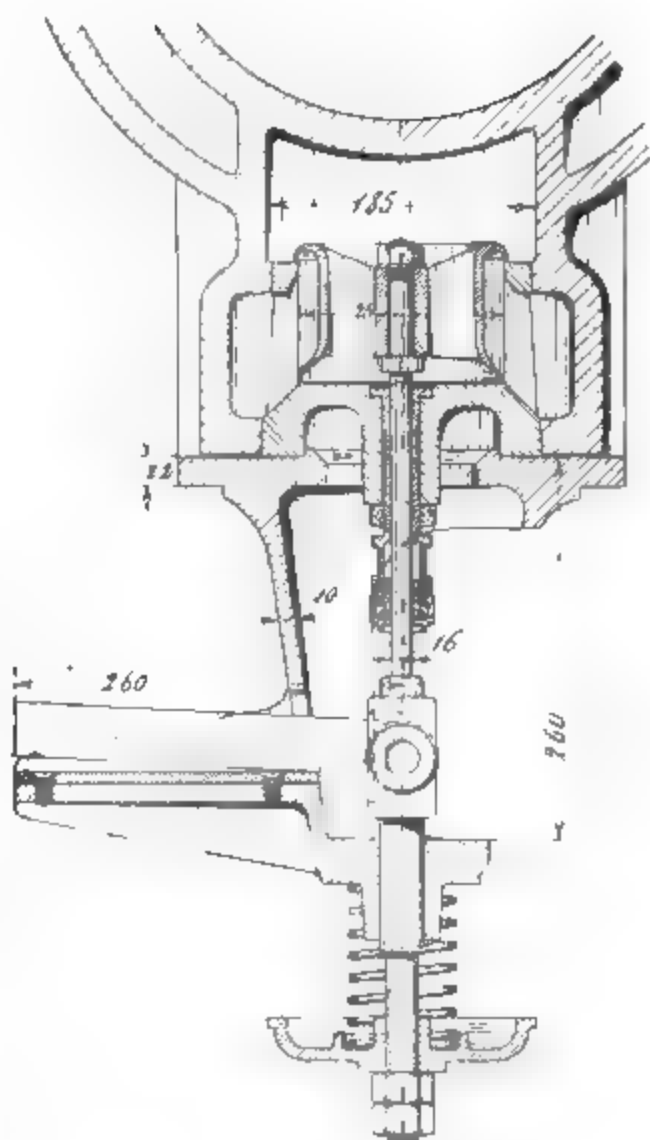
Auslassventil für Maschine von 350 Durchmesser.
